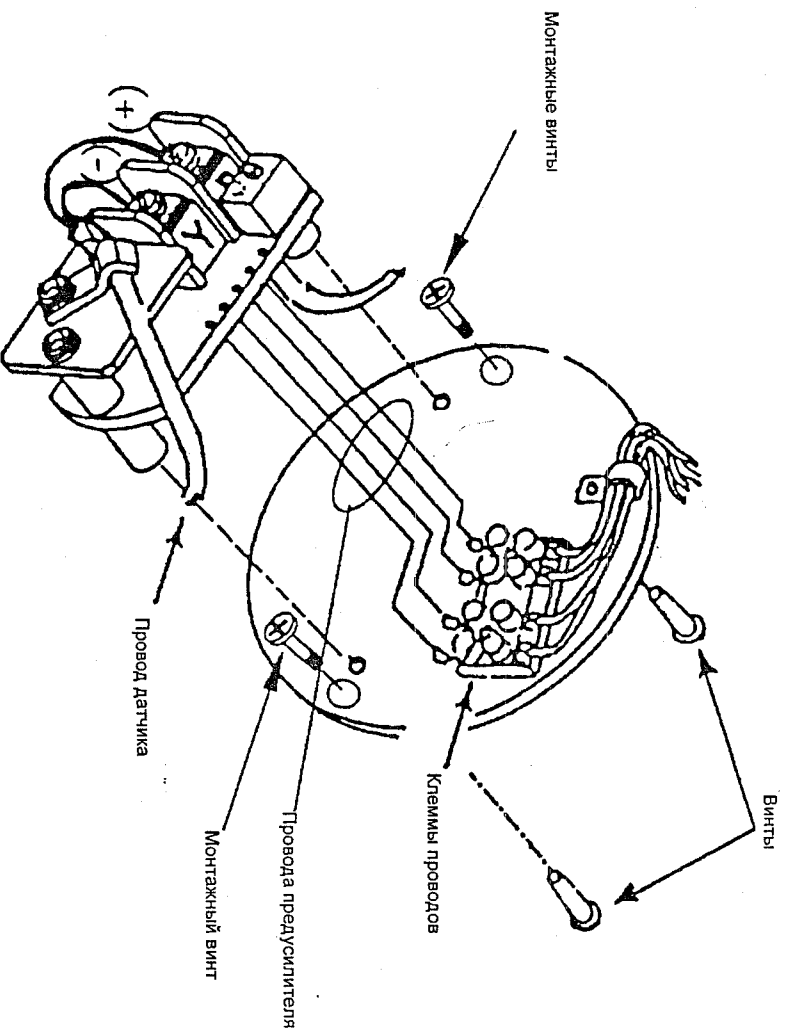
Узел предварительного усилителя – схема раздельного монтажа
